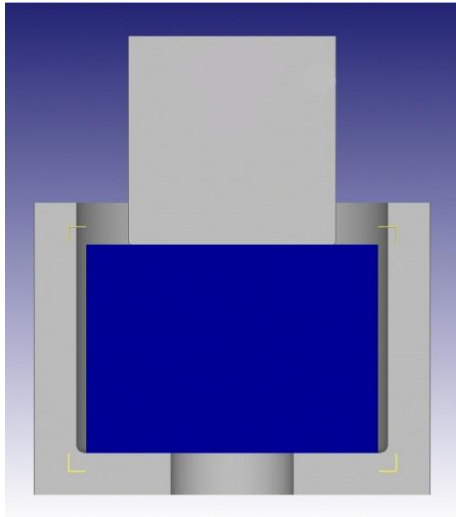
Исходное положение заготовки и рабочего инструмента
